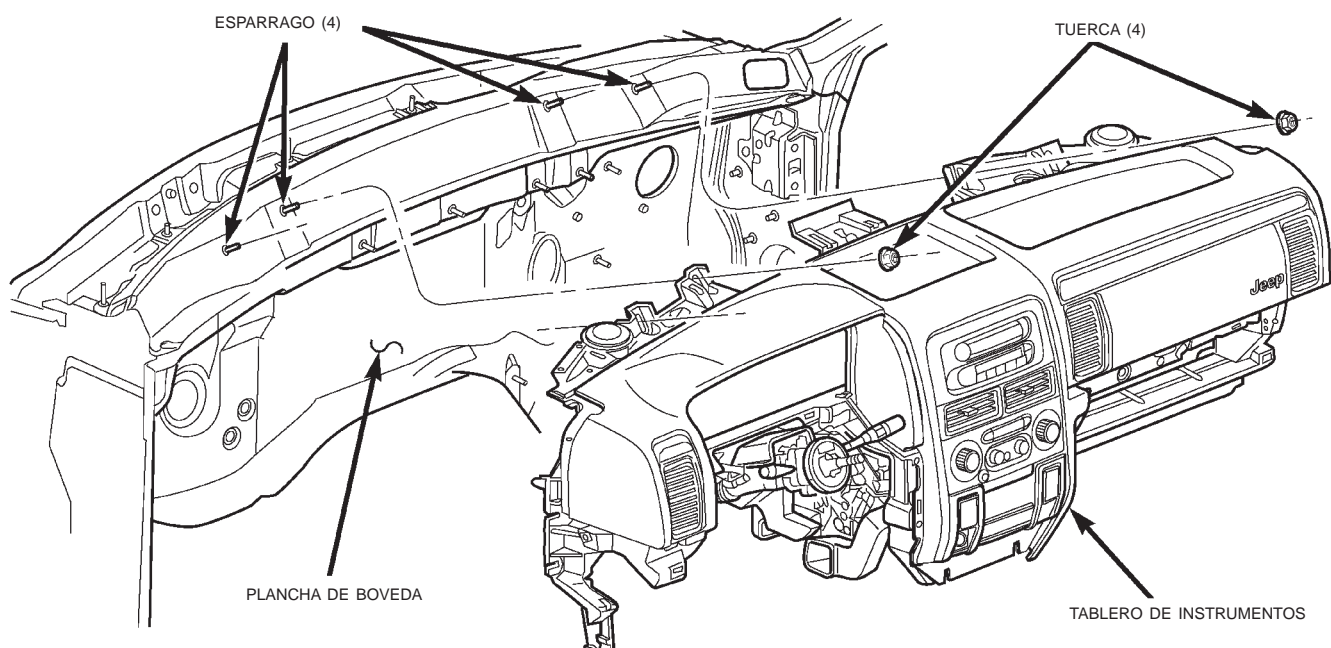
Montaje del tablero de instrumentos a la plancha de bóveda
